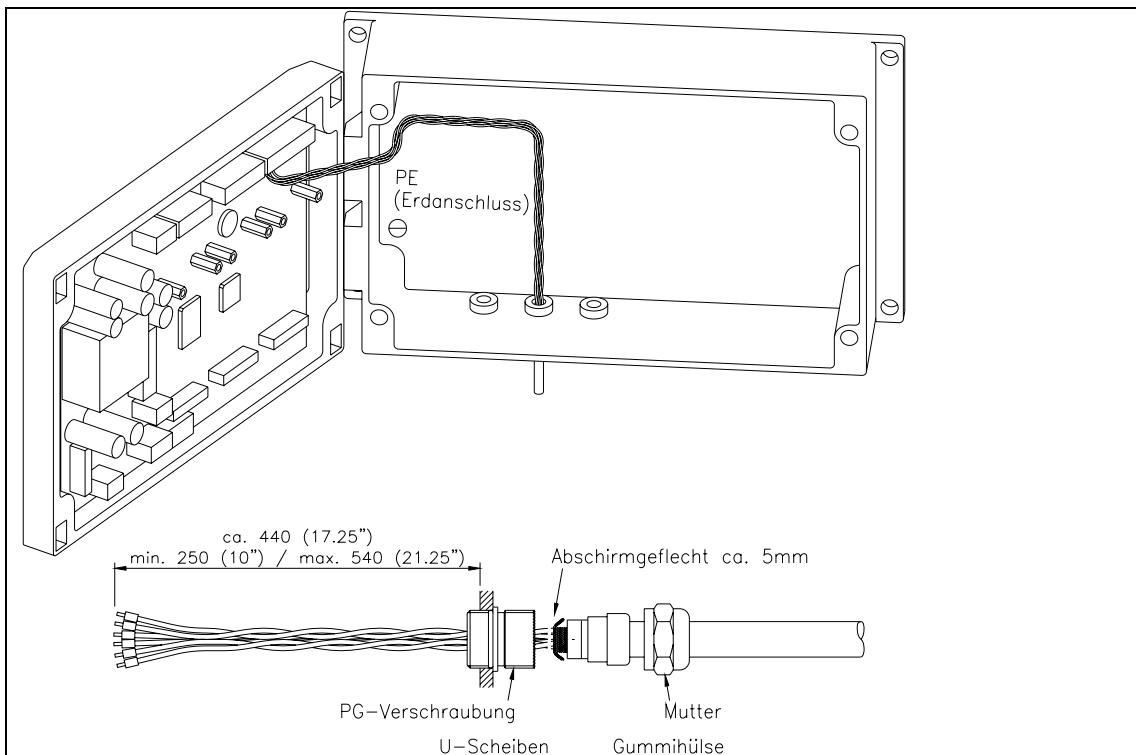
Verlauf der Anschlusskabel im Gehäuse
